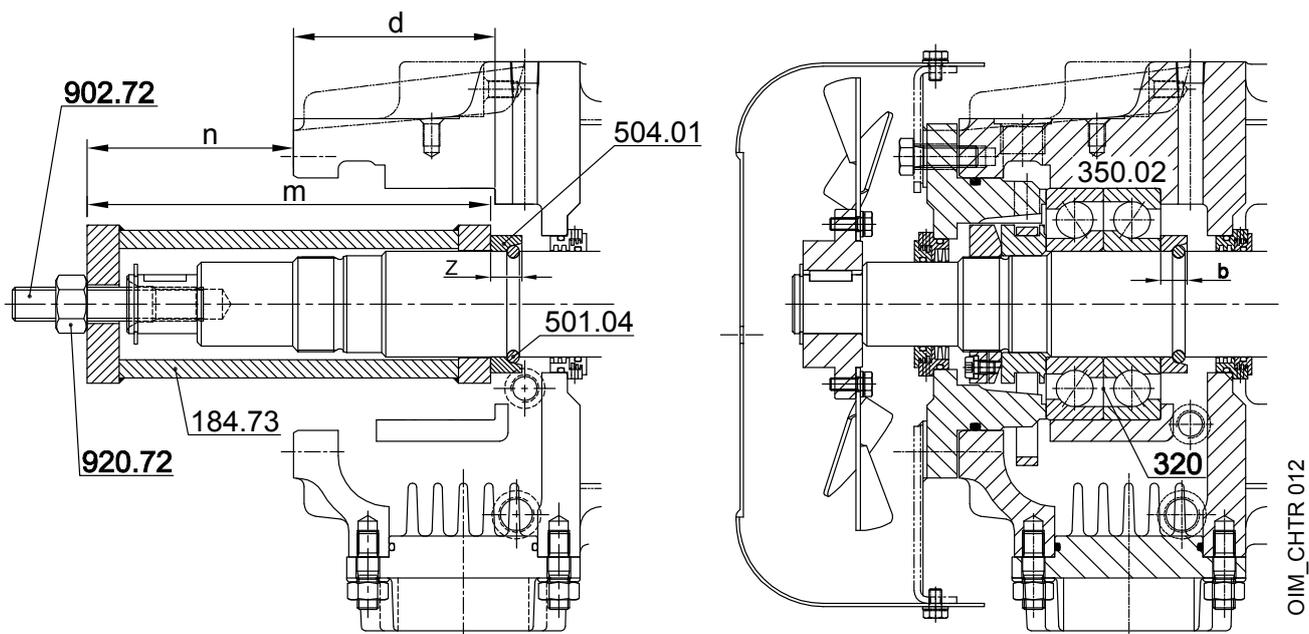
Отрегулировать упорный подшипник CHTR 2-3 (радиально-упорный шарикоподшипник)
